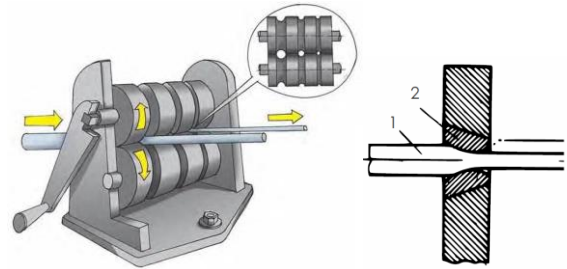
Схема волочіння дроту: 1 – заготовка; 2 – фільтра; 3 – готовий виріб
